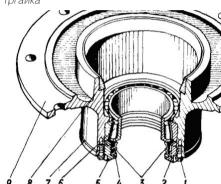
Разборка картера: 1 — бо лт; 2 шайба; 3 — манжета; 4 — ко льцо; 5 — крышка; 6 — подшипник; 7 — прокладка; 8 — обойма наружная подшипника; 9 — картер
